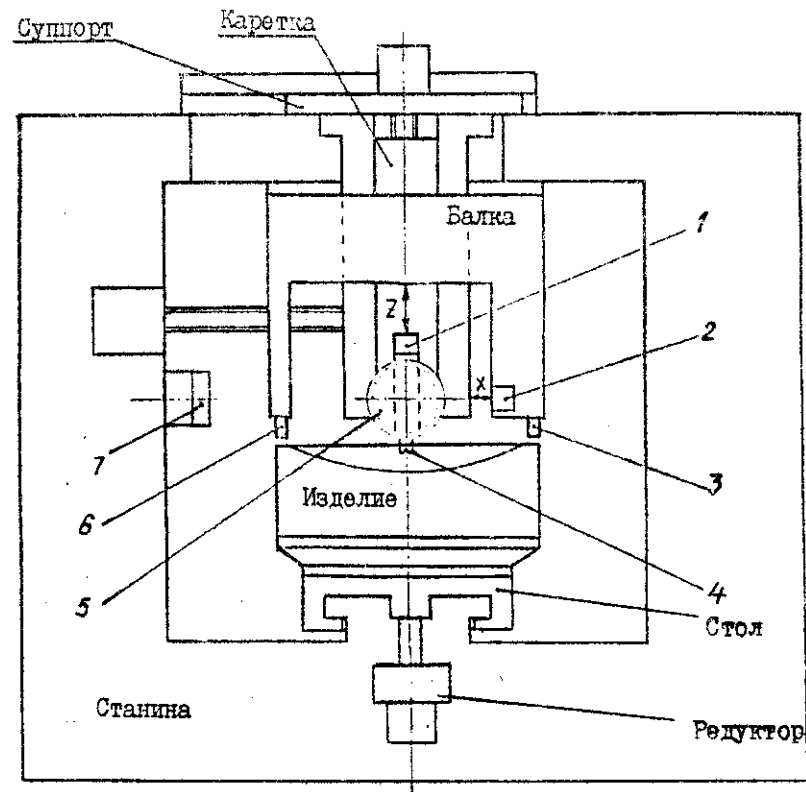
Схема специального сверхточного шлифовального станка мод. МШ356
